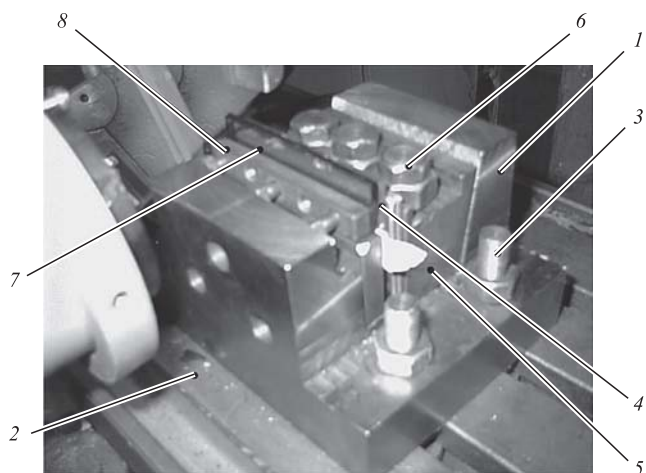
Приспособление, установленное на столе горизонтально-фрезерного станка
